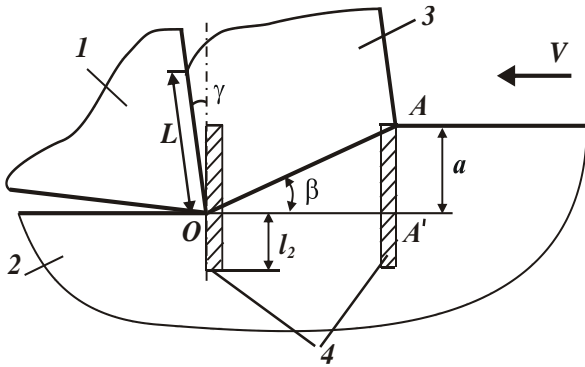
Расчетная схема процесса точения: 1 – резец; 2 – обрабатываемый материал; 3 – образующая стружка; 4 – адиабатический стержень.
